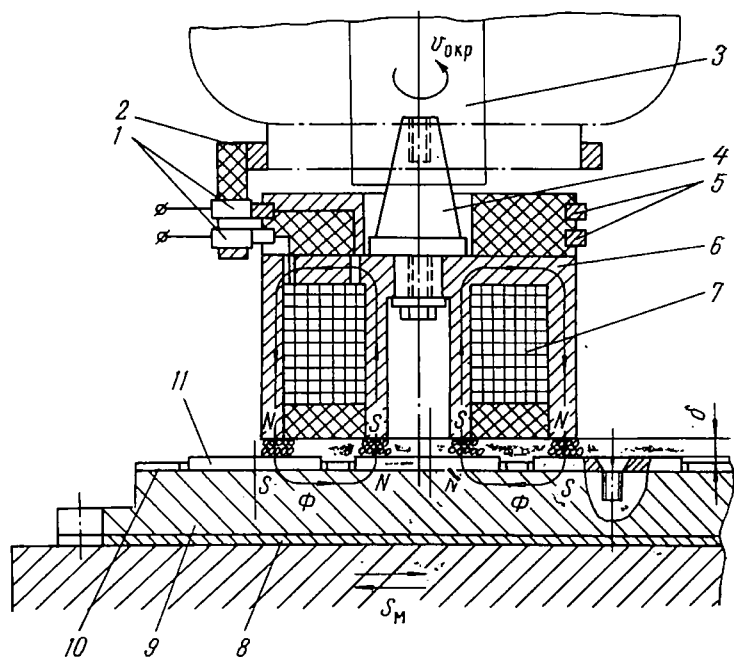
Схема устройства для обработки плоскостей торцом магнитного барабана
